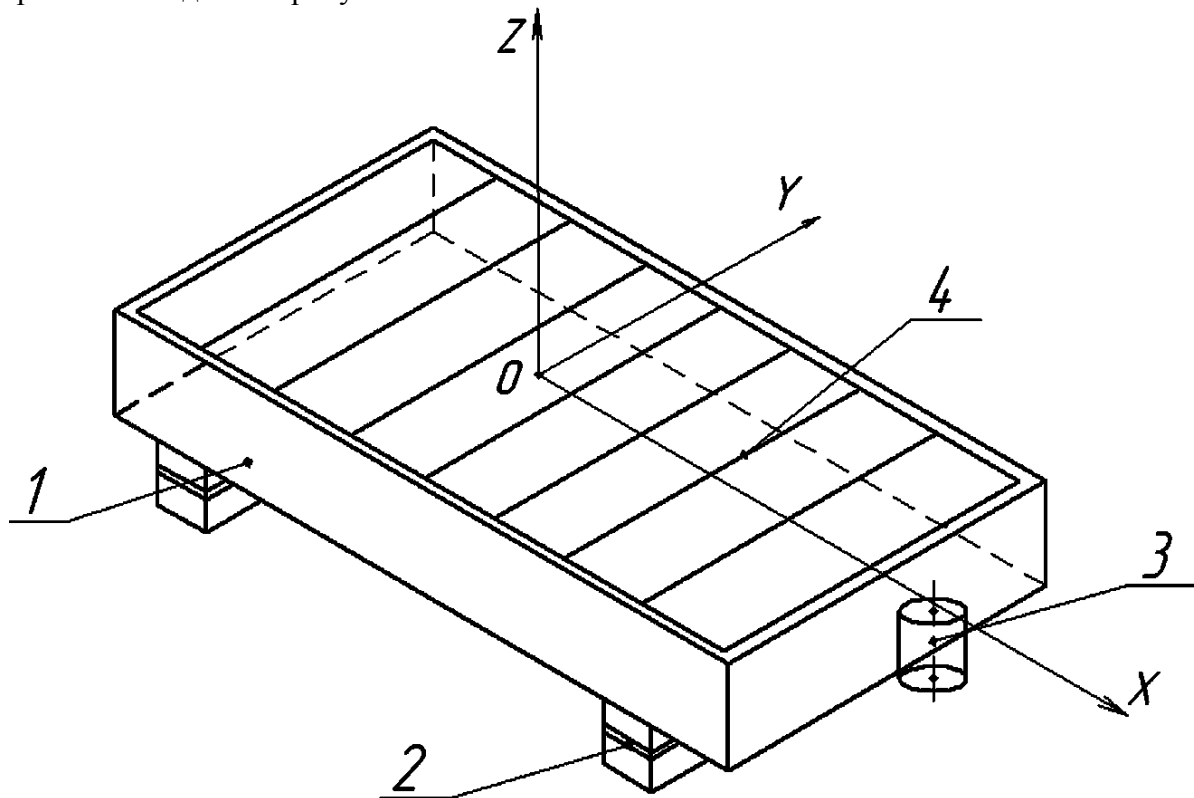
Схема вібраційної установки з активним робочим органом: 1 – металева форма; 2 – пружна опора; 3 – вібробуджувач; 4 – активний робочий орган (пластина)
